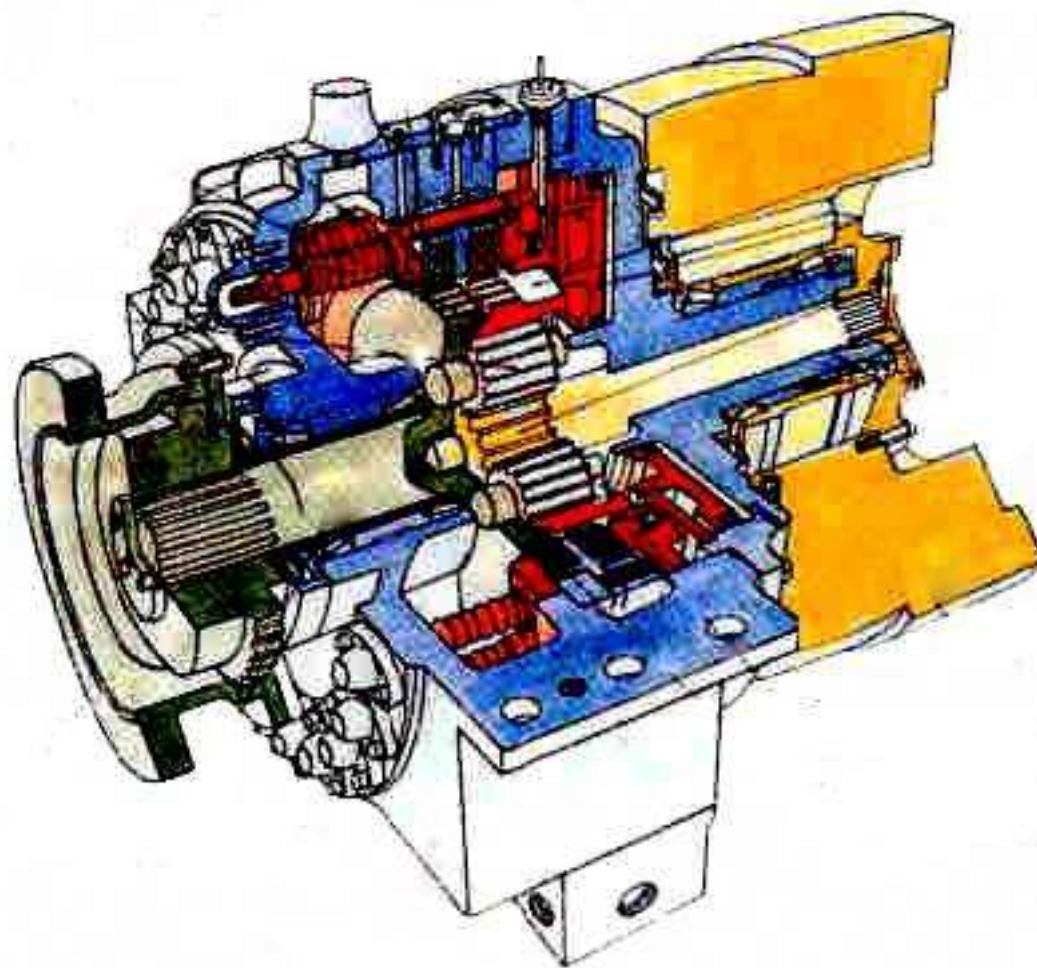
Планетарный привод «TORC-PAC»
